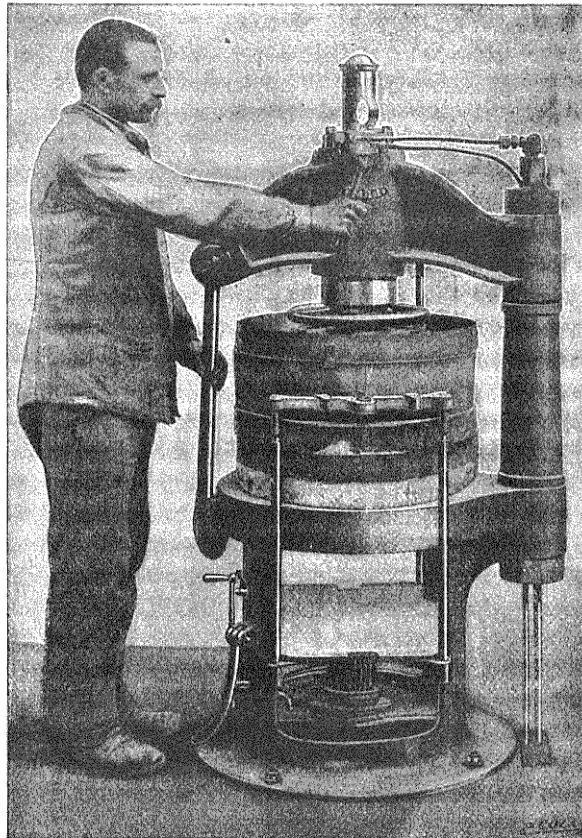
Machine à mouler Bonvillain et Ronceray de type courant.
